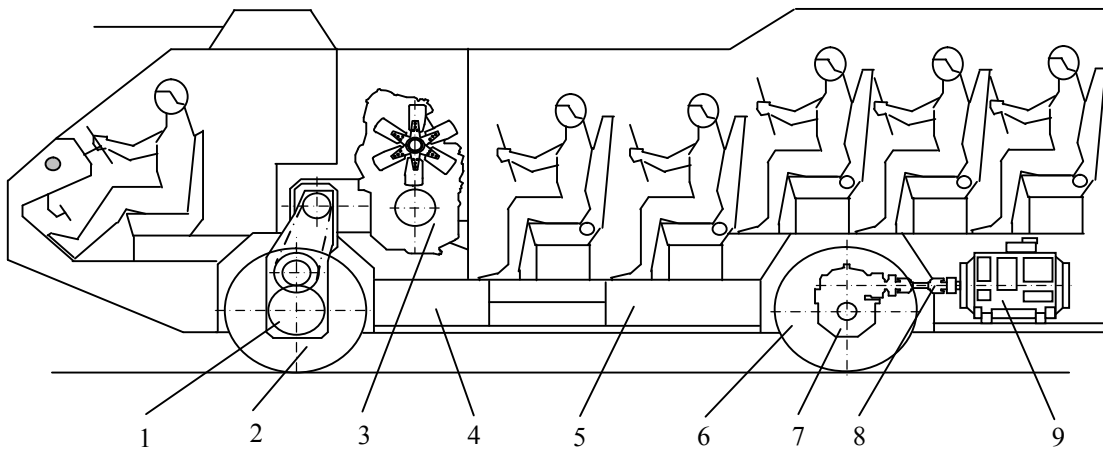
Конструктивна схема бронетранспортера: 1- редуктор переднього ведучого моста; 2 - переднє колесо; 3 - силова установка; 4,5 - блок акумуляторних батарей; 6 - заднє колесо; 7 - редуктор заднього ведучого моста; 8 - карданний вал; 9 - електричний двигун
